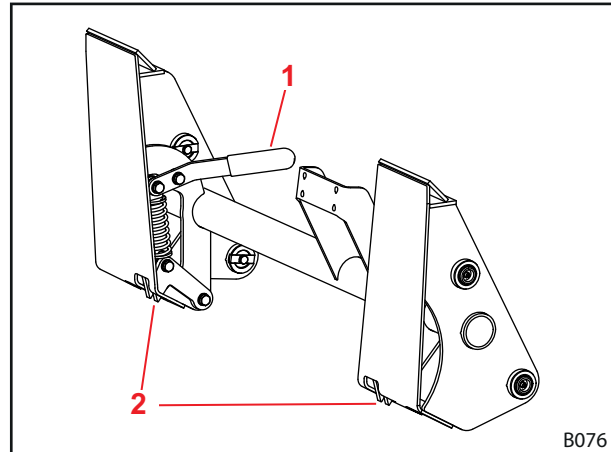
Verrouillage des outils sur des cadres porte-outils Skid-Steer
